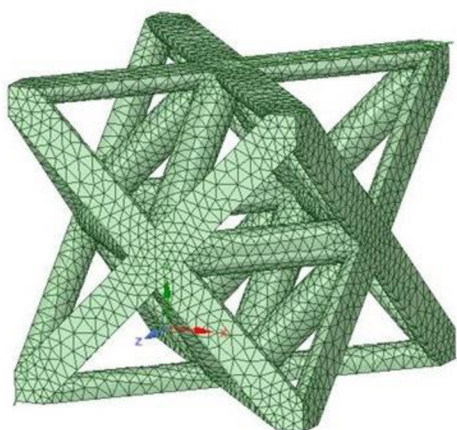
Ligamenty vytvorené odstránením povrchových plôch.
